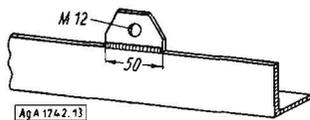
Richtig angeschweißtes Halterungsblech
